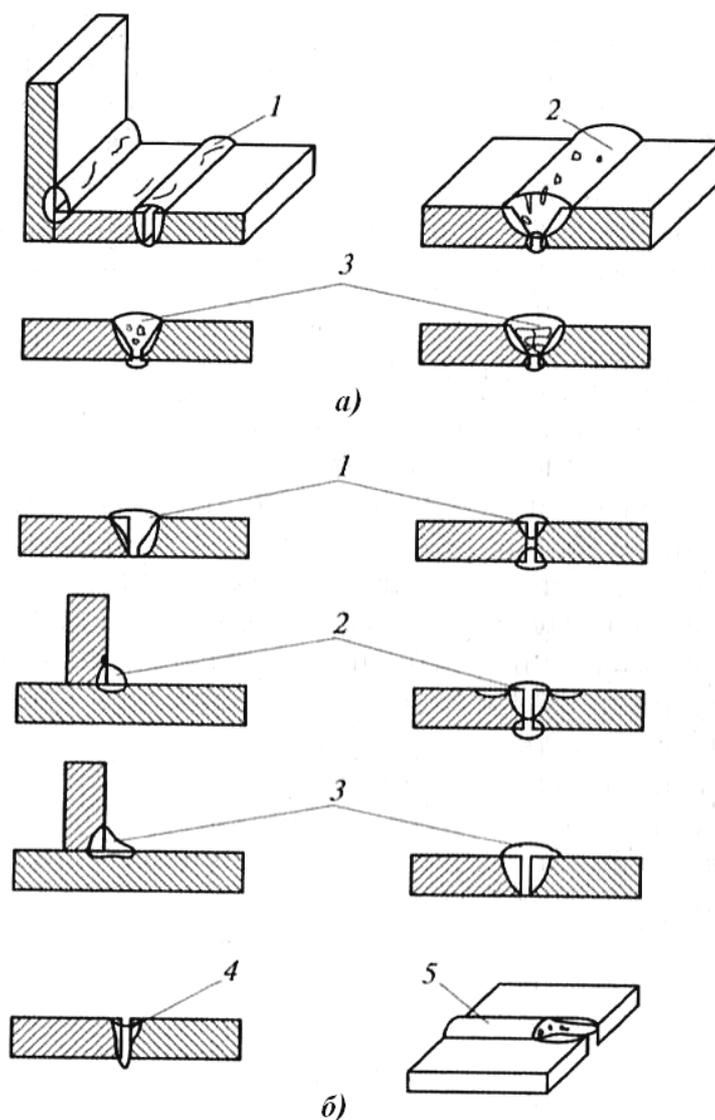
Виды дефектов сварных швов: а – связанные с металлургическими процессами: 1 – трещины; 2 – поры и свищи; 3 – шлаковые включения; б – связанные с нарушениями режима сварки: 1 – непровары; 2 – подрезы; 3 – наплывы; 4 – вогнутость шва; 5 – прожоги
